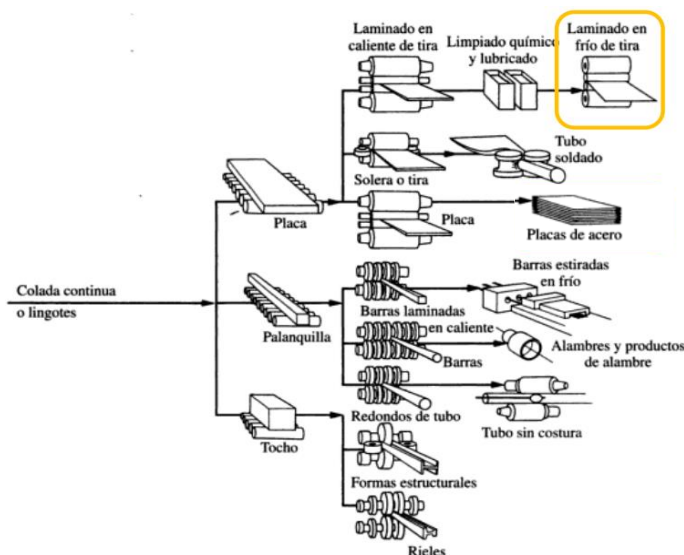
Esquema proceso de fabricación (destacando en amarillo la chapa para bobinado)
